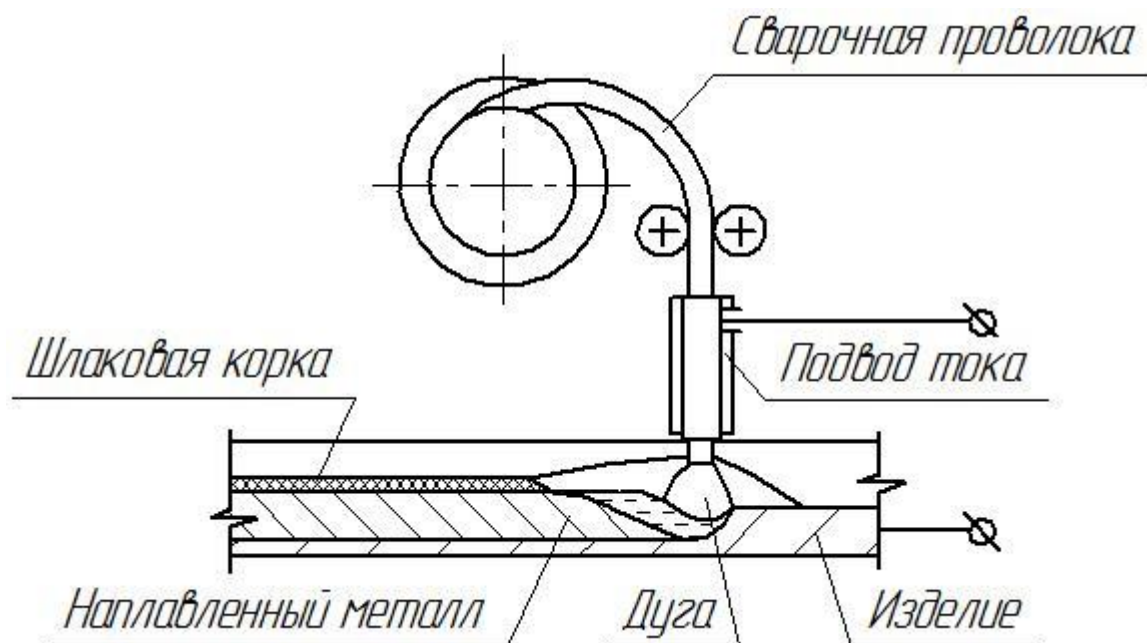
Схема восстановительной наплавки порошковой проволокой
